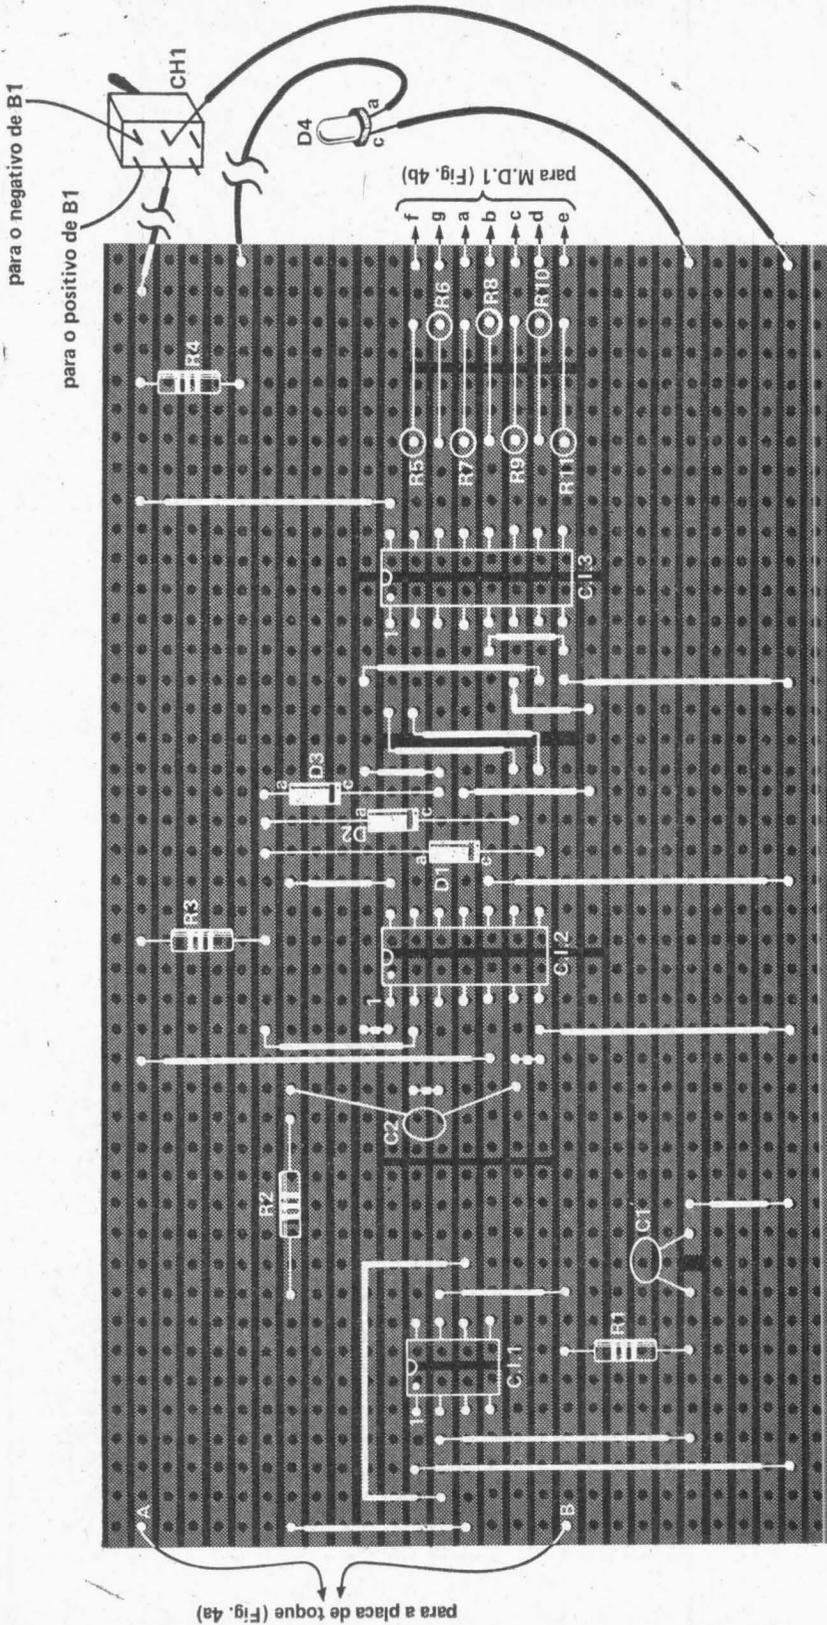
Disposição dos componentes sobre a plaqueta da Fig. 2 CH1, M.D.1, D4 e a placa de toque foram fixados à caixa do aparelho.
